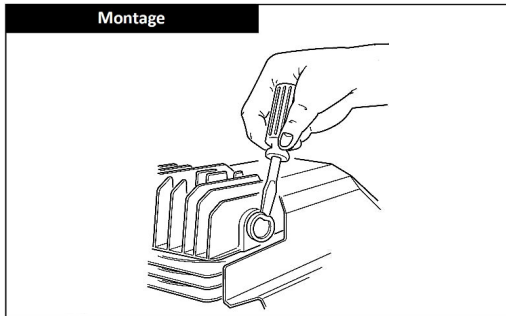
Kompressorkopf-Abdeckung für Filtermontage entfernen
